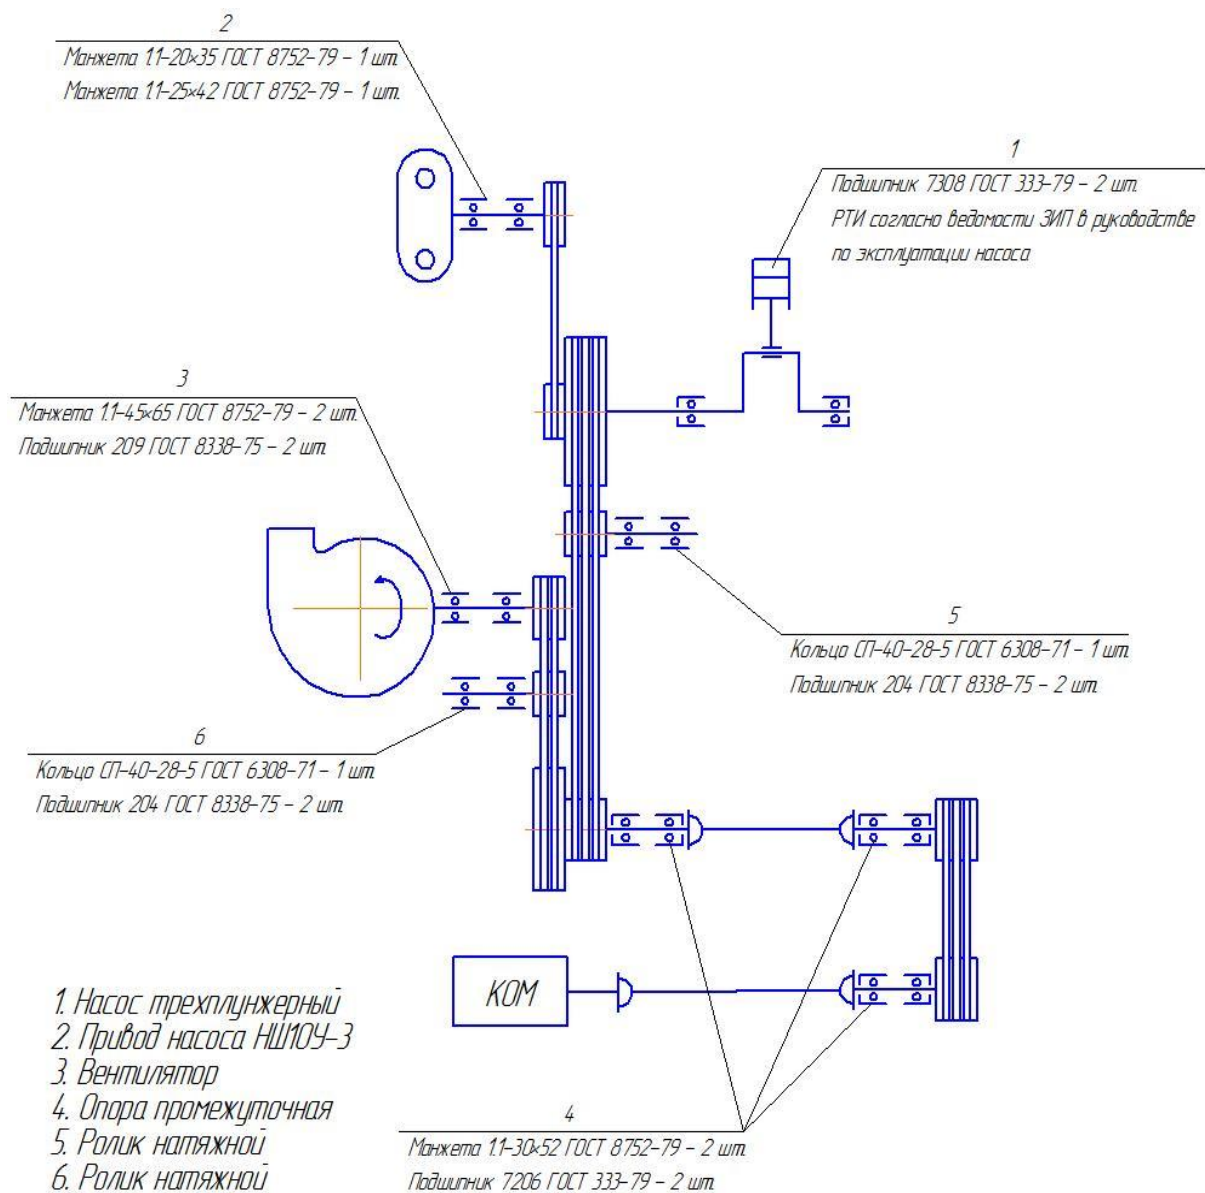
а – Схема расположения подшипников и уплотняющих быстроизнашивающихся изделий с питательным насосом 1.1ПТ-25М2
